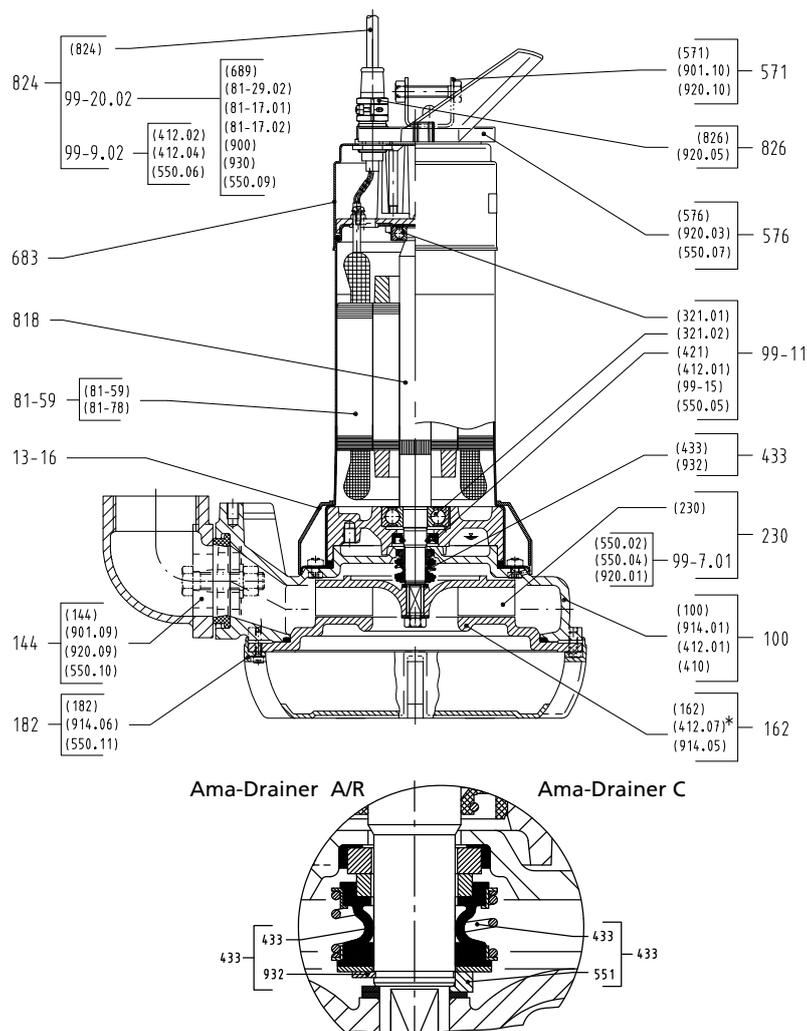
Сборочный чертеж Ama-Drainer 522/11
